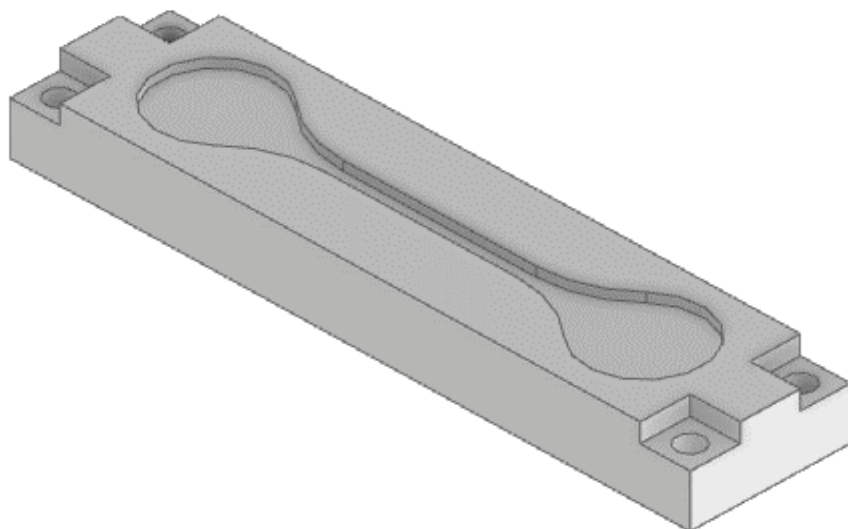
Vytvoření základních rozměrů testovací geometrie
